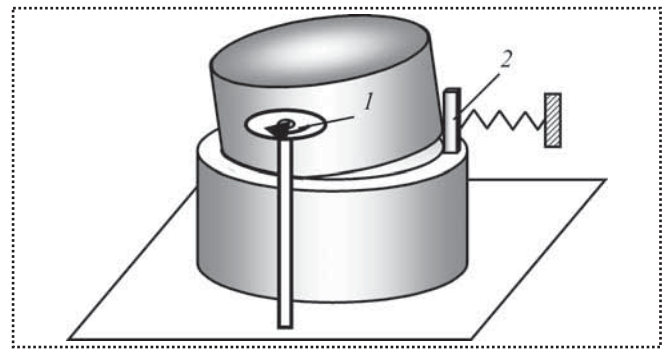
Устройство для вертикальной сборки цилиндрических деталей
